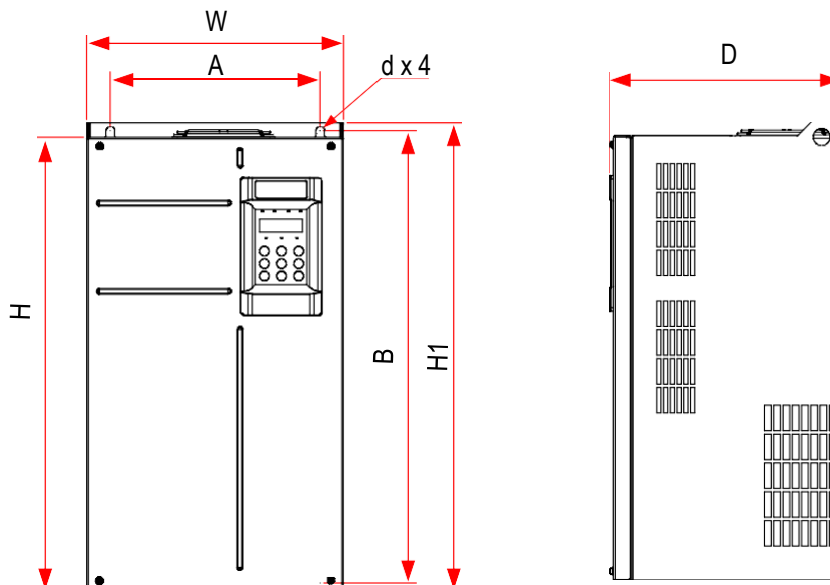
GT600-4T45G(B)~GT600-4T160G 外型尺寸及安装尺寸示意图
